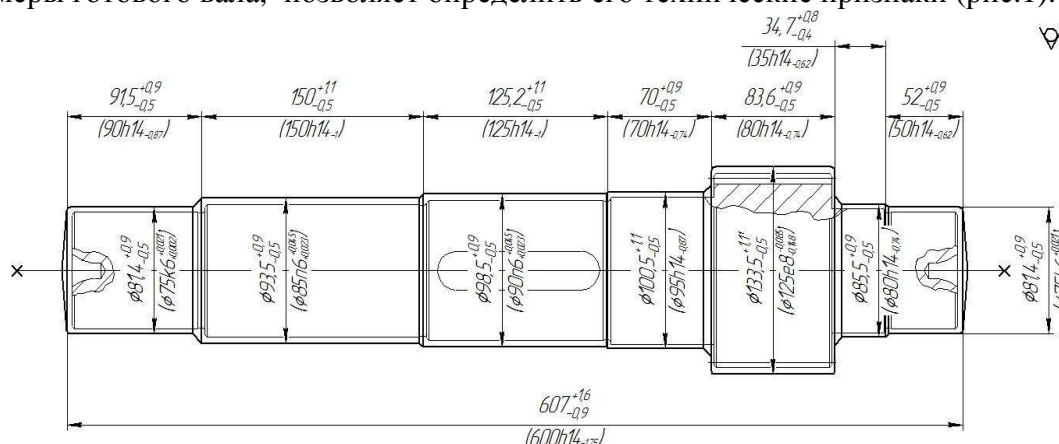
Эскиз штампованной заготовки вала шлицевого (поковки)
